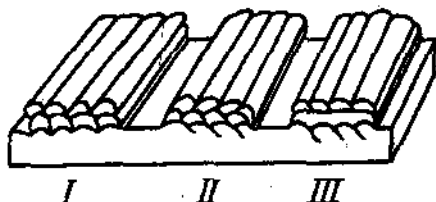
Образцы неправильной и правильной наплавки металла валиками.
